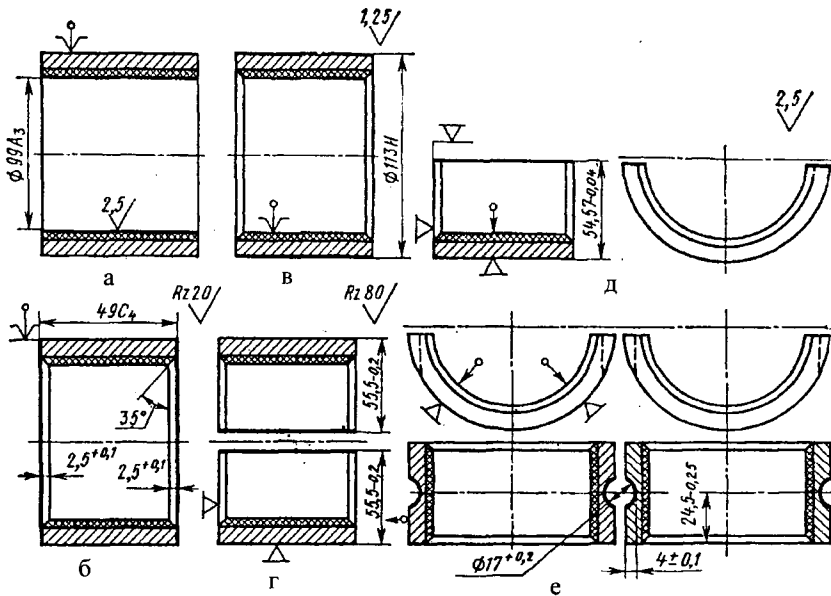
Технологічна схема механічної обробки вкладиша нижньої головки шатуна поршневого компресора АУ-200.
